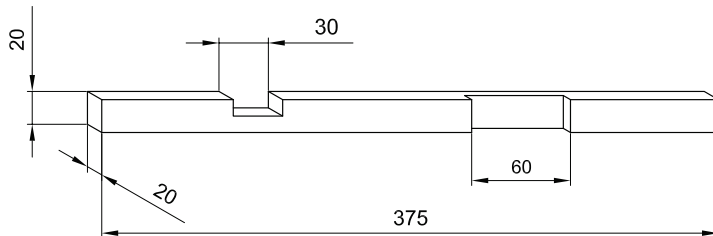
Piso de la colmena Langstroth (medidas en mm)
